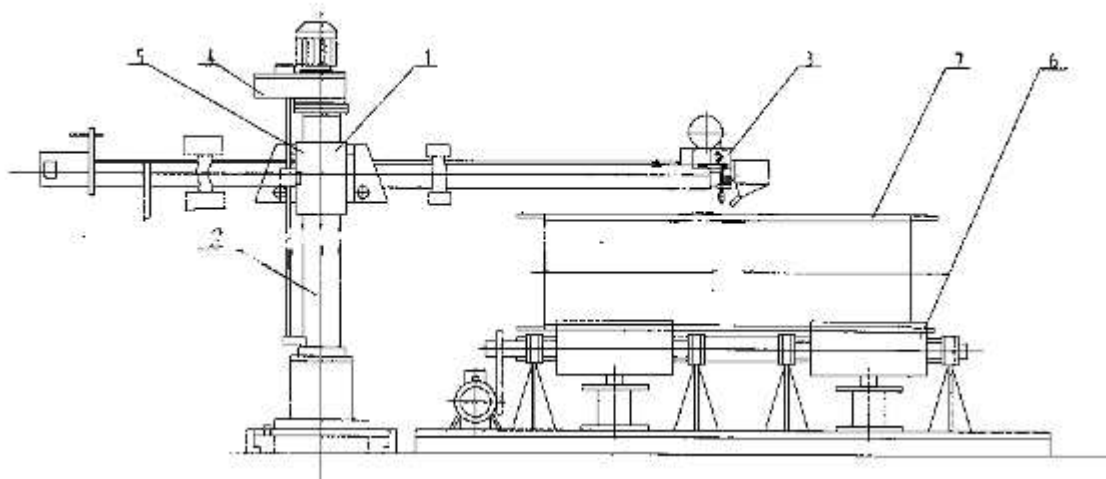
Установка 2/RMB2.0x2.0 для автоматической сварки продольных стыков обечаек
